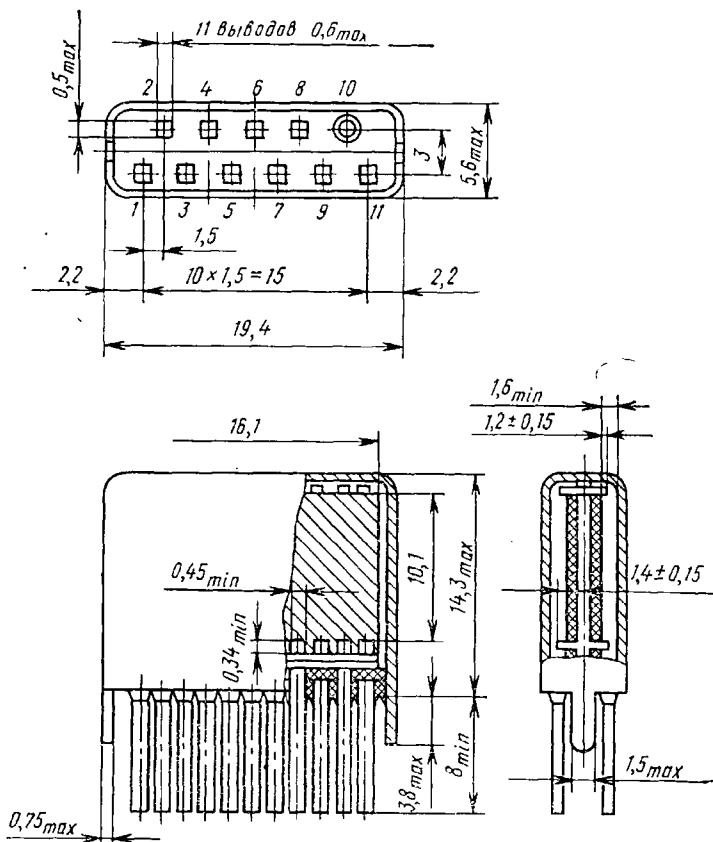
Конструкция металлополимерного корпуса «Акция»
